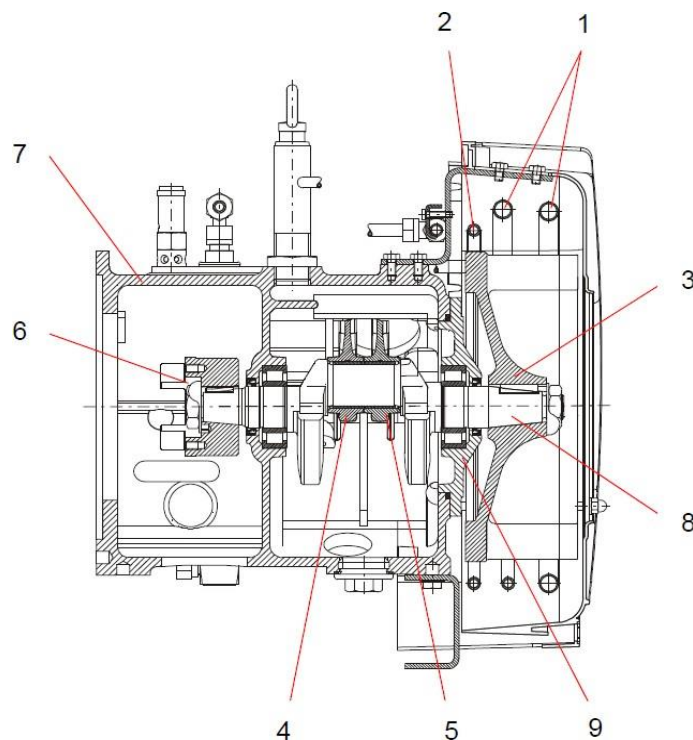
Будова компресора WP 22L: 1 - вентилятор першої ступені; 2 - вентилятор другої ступені; 3 - колесо вентилятора, маховик; 4 - шатун першої ступені; 5 - шатун другої ступені; 6 - гнучка муфта з на пів муфтою компресора; 7 - корпус; 8 - колінчастий вал; 9 - корпус підшипника
